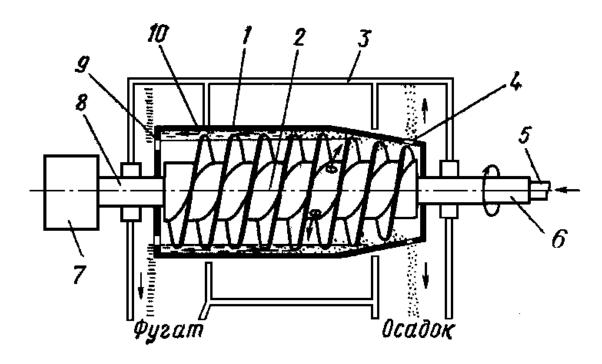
Принципиальная схема устройства центрифуги типа ОГШ: 1 — цилиндроконический ротор; 2 — шнек; 3— неподвижный кожух; 4 — разгрузочные окна для осадка; 5 — питающая труба; 5 — вал ротора; 7 — планетарный редуктор; 8 — вал шнека; 9 — сливные окна для фугата; 10 -жидкостный объем ротора.
